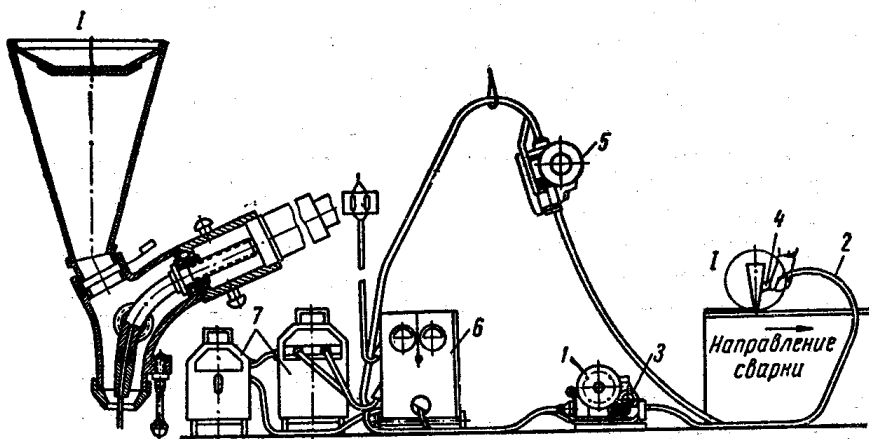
Полуавтомат для сварки под флюсом:
